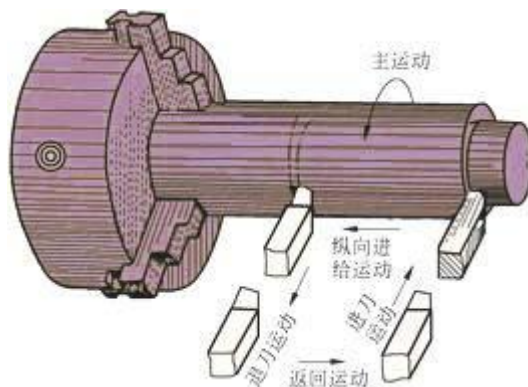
车削运动车床主要用于加工回转体表面（图 1-2），加工的尺寸公差等级为 IT11~IT6，表面粗糙度 Ra 值为 12.5~0.8 μm 。车床种类很多，其中卧式车床应用最为广泛。
